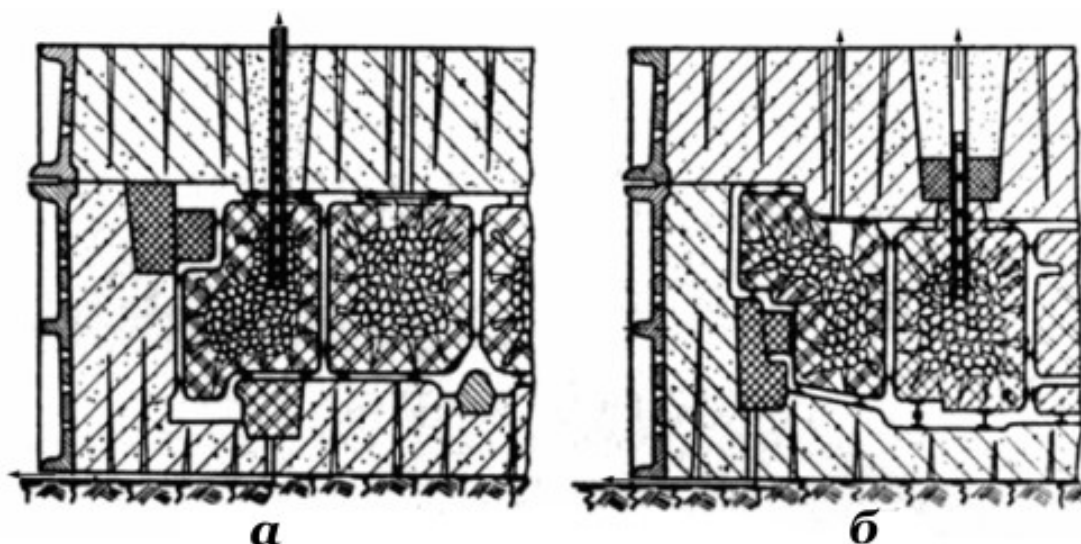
Вывод газов из собранной формы через трубки: а – с засыпкой вентиляционного колодца; б – с установкой стержня в вентиляционный колодец
